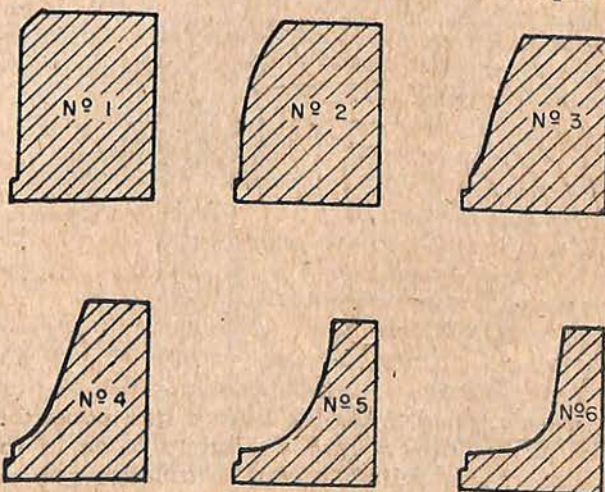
Plantillas tomadas del plano de formas transversales.
